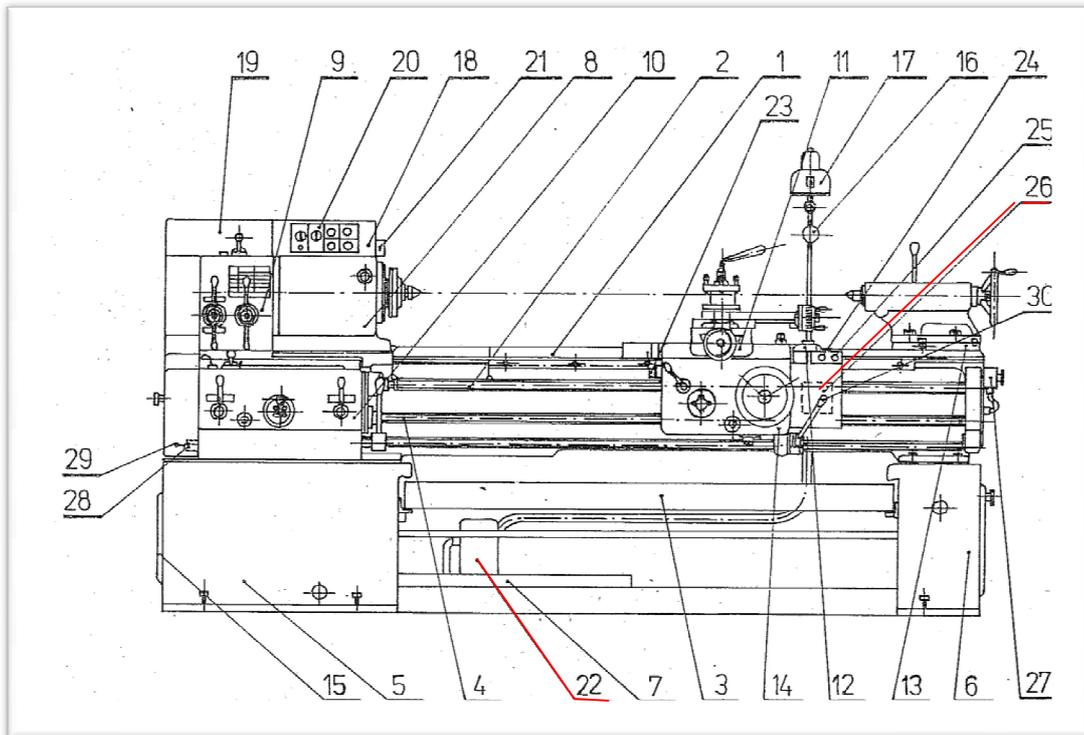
Description des sous-ensembles et des pièces de machine [5]
